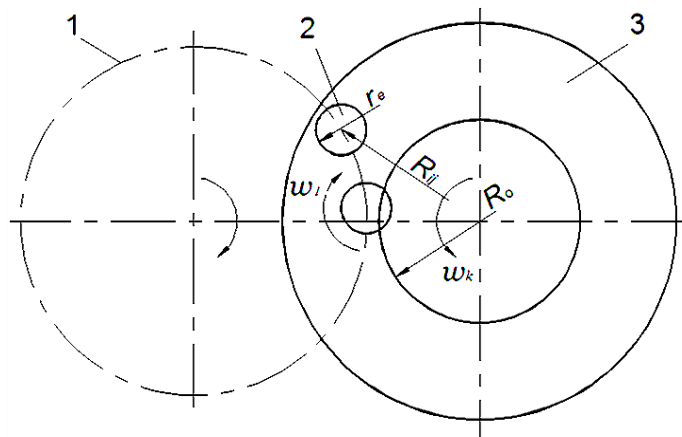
Схема обработки свободных заготовок с круговой подачей:
